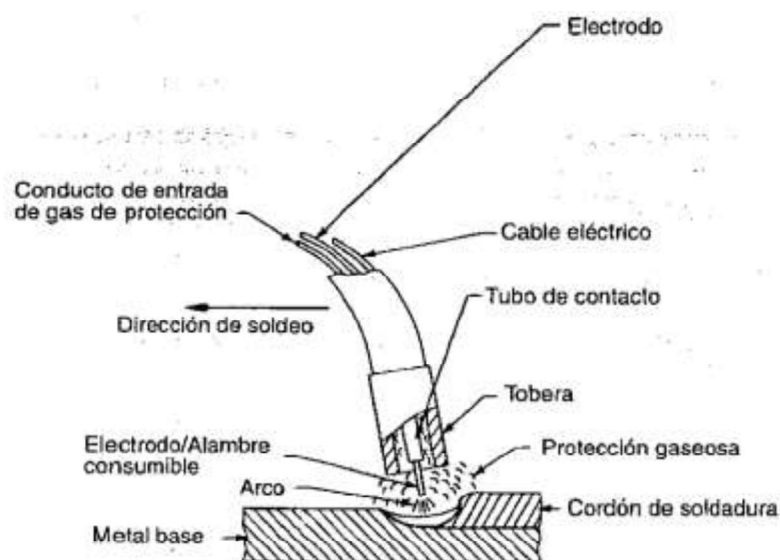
Elementos que componen la soldadura por arco con gas de protección.
